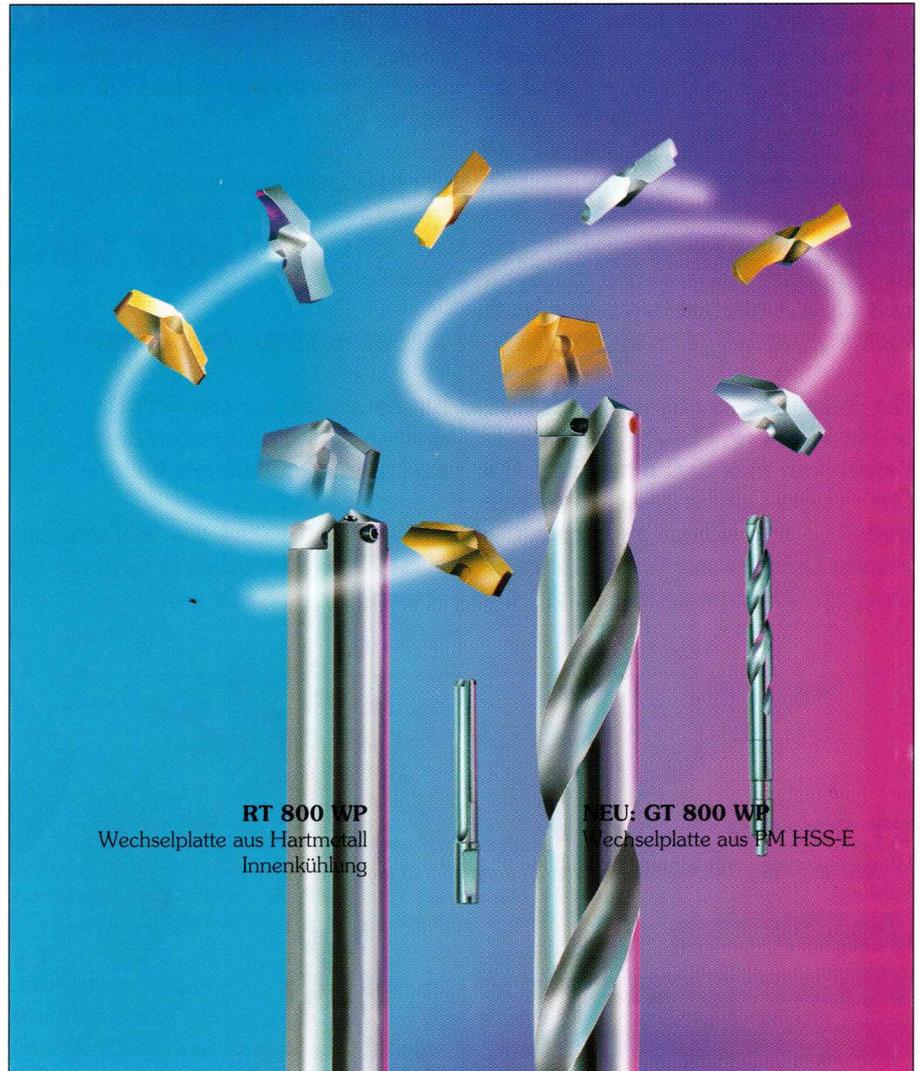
Das Werkzeugsystem T 800 - durchgängig die wirtschaftliche Alternative zu HM- und Schnellstahl-Bohrern > Ø 16 mm.
